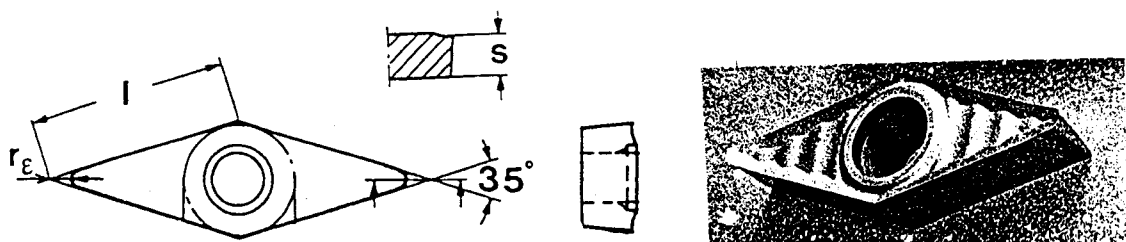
Géométrie de la Plaquette VCGX utilisée pour l'usinage du composite F3K10S [124].
